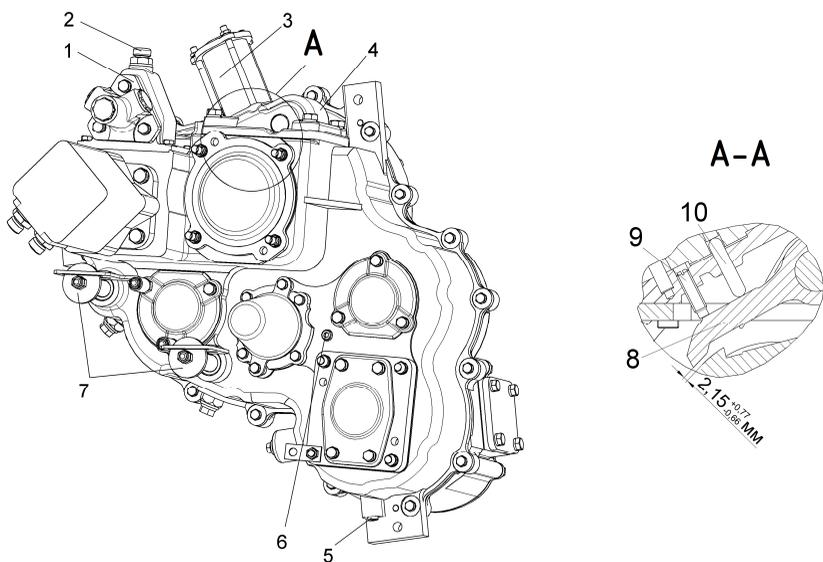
Коробка передач привода питающего аппарата (вид слева):
